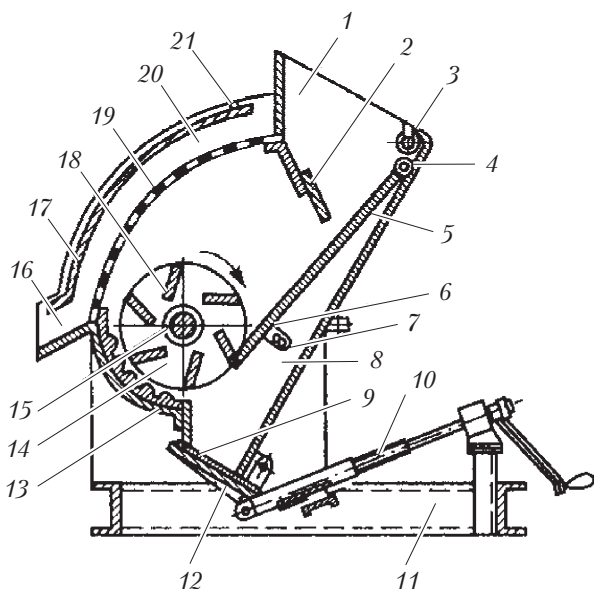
Схема фрезерно-струйной мельницы ФСМ-7:
